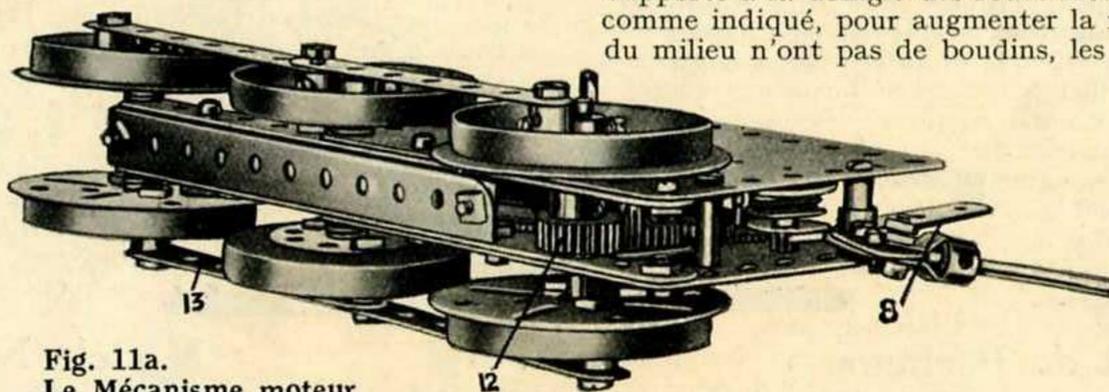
Le Mécanisme moteur du modèle vu d'en bas.
